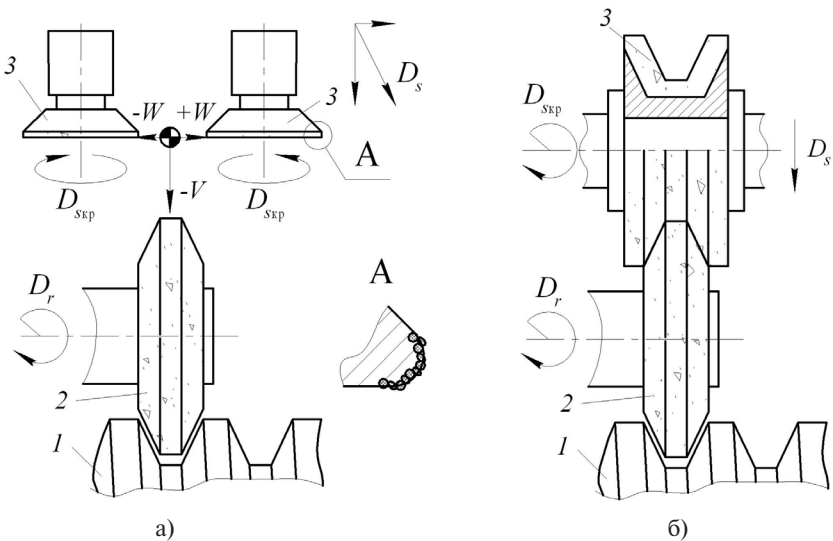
Алмазная правка круга обтачивающим (а) и профильным (б) роликами: 1 – заготовка; 2 – шлифовальный круг; 3 – ролик; 4 – алмазный слой
